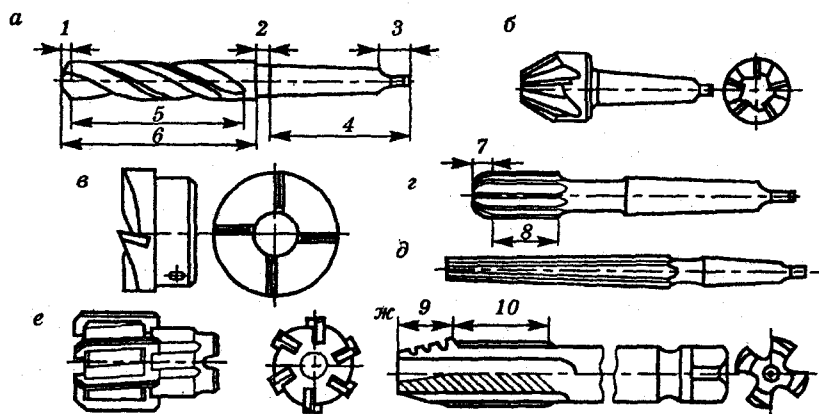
Инструмент для обработки отверстий на сверлильных станках: а–в — зенкеры; г–е — развертки; ж — метчик
